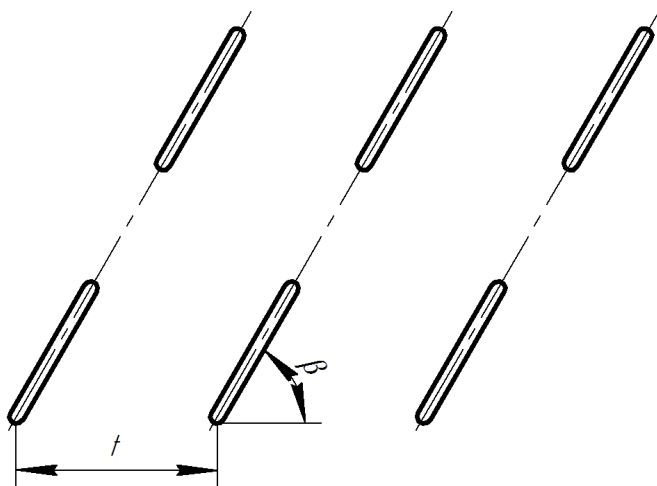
Схема розташування гумових рифлів на поверхні труби шнека
